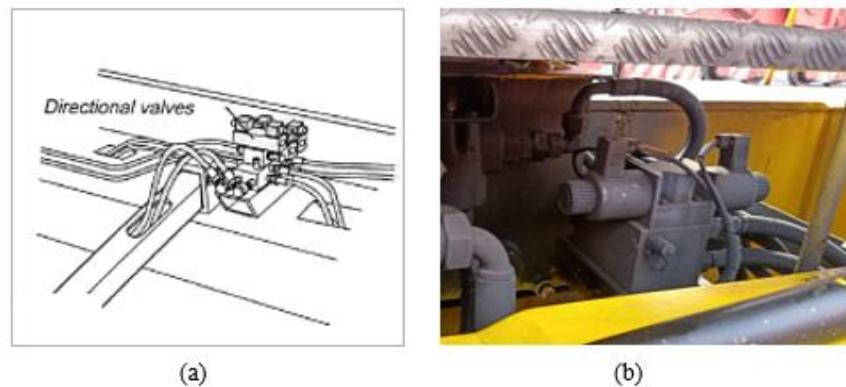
76 Power Pack atau Unit Hydraulic pada Spreader
